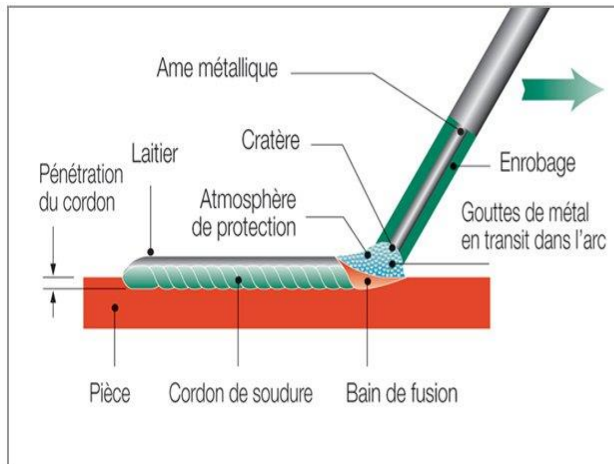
Schéma de procédure de soudage à l'arc enrobée
